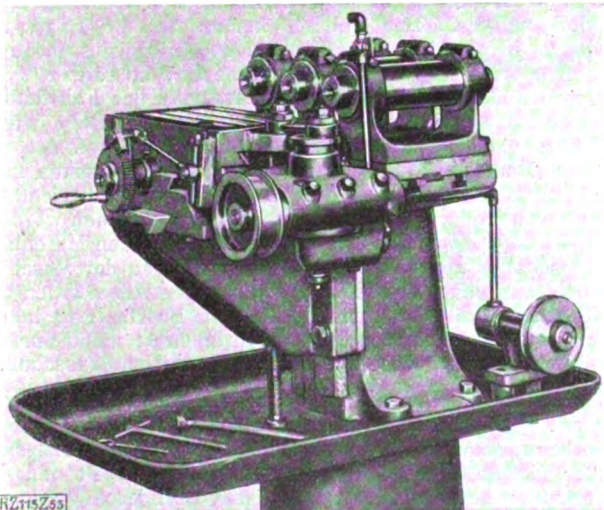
Dreispindlige Langlochfräsmaschine für Massenteile.
